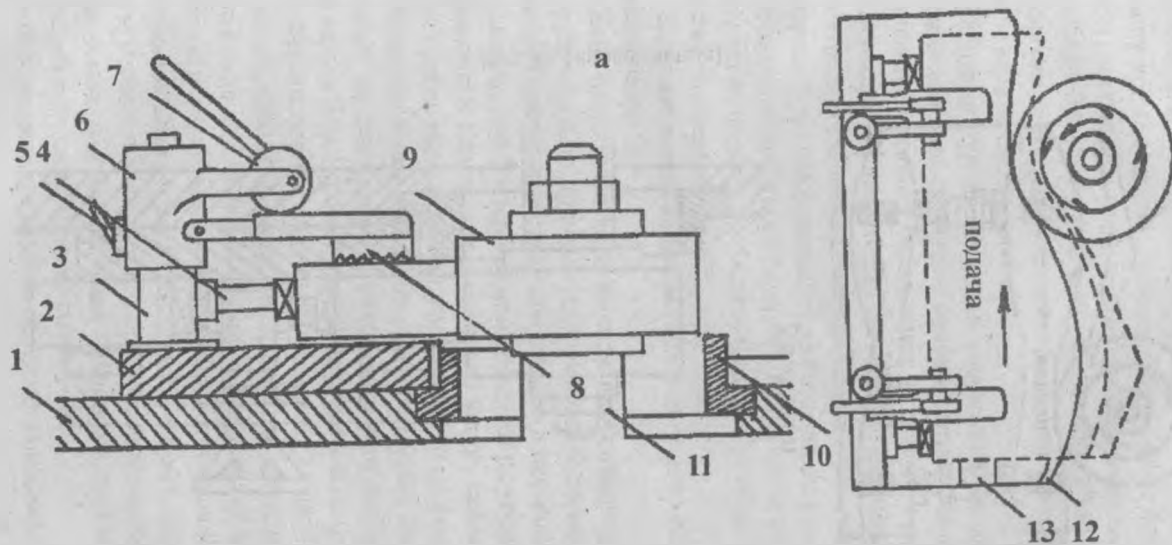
Схема криволинейной обработки на фрезерном станке с помощью шаблона:
